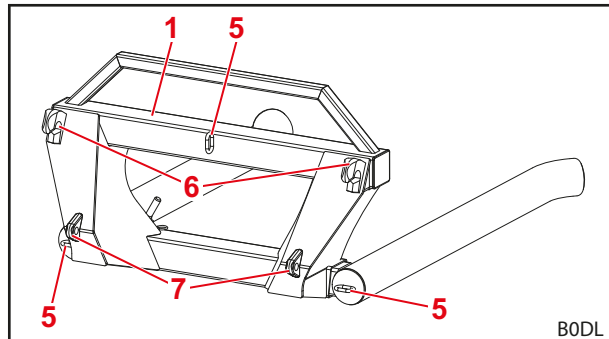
Конструкция вилок для перевозки тюков H – вид сзади
